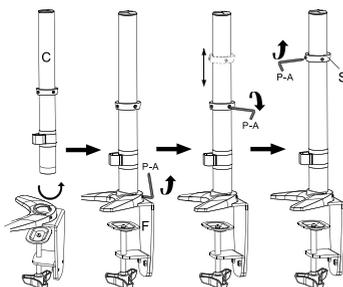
Montaggio Tavolo - Pre-assemblaggio 1
